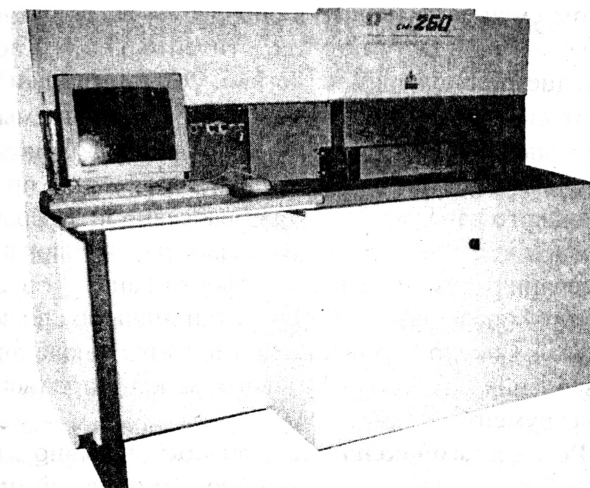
Установка ЭМ-260 для автоматической лазерной обточки и распиловки заготовок ювелирных алмазов.
